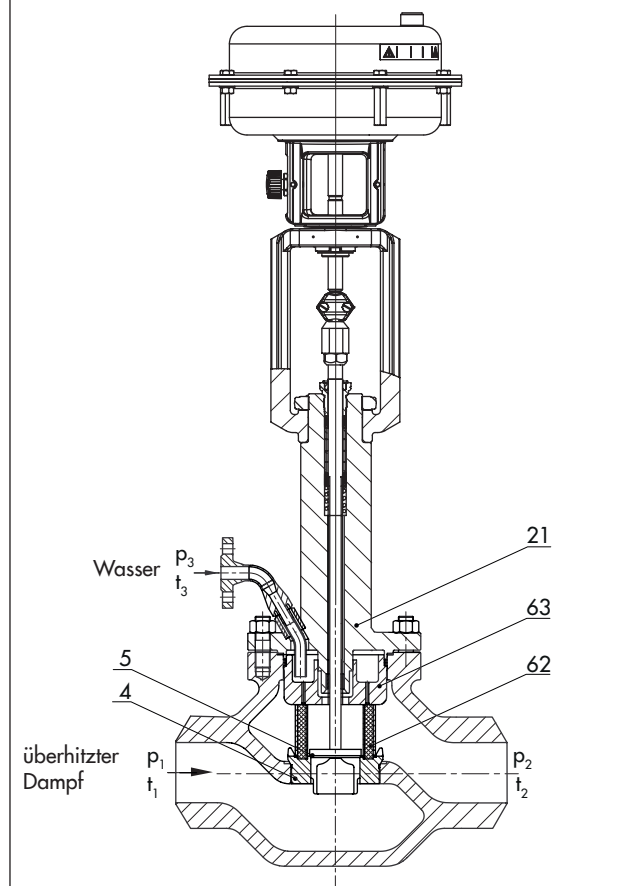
Pneumatischer Dampfumformer Typ 3281-7 mit Isolierteil, Anschweißenden und Antrieb Typ 3277
